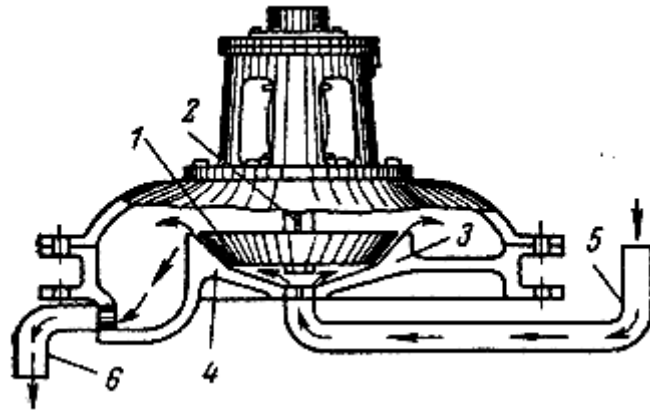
Схема колоїдного млина: 1 — конічний диск ротора; 2 — вал ротора; 3 — статор; 4 — пришліфовані робочі поверхні [7]
